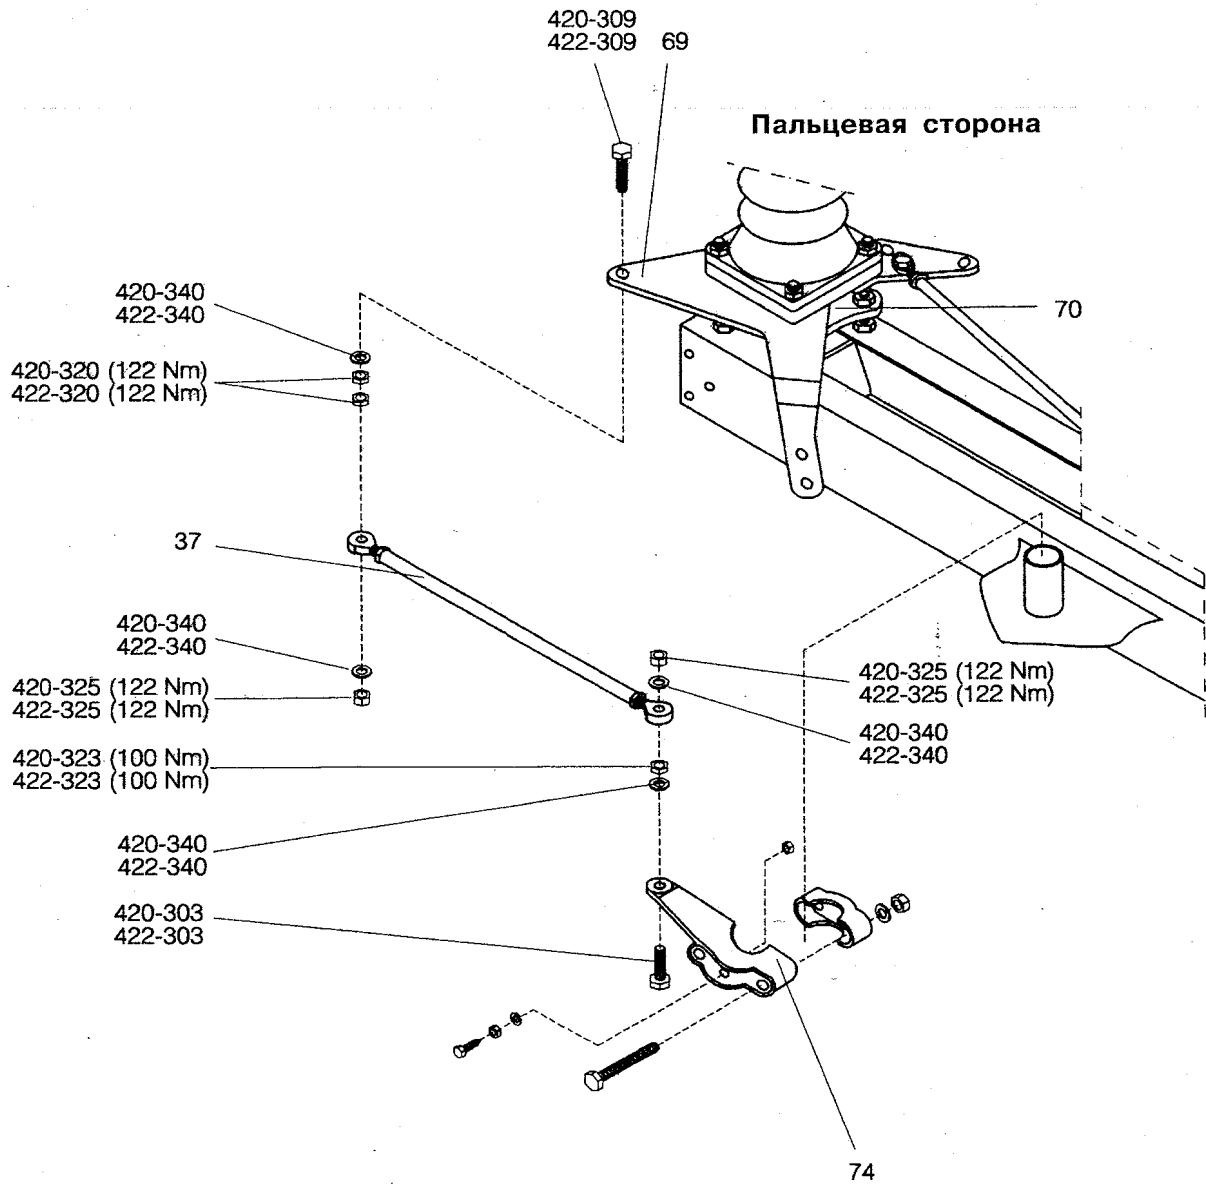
Установка тяг разъединителя; установка приводной тяги (37) при расположении приводного механизма разъединителя на стороне противоположной открыванию
